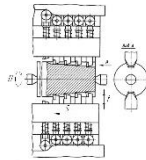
Схема одночасної обробки зубів валу струганням багаторізцевою головкою
